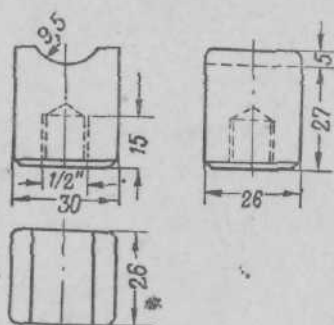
Подшипники к осям нижних (вытяжных) валиков ватеров сухого прядения
